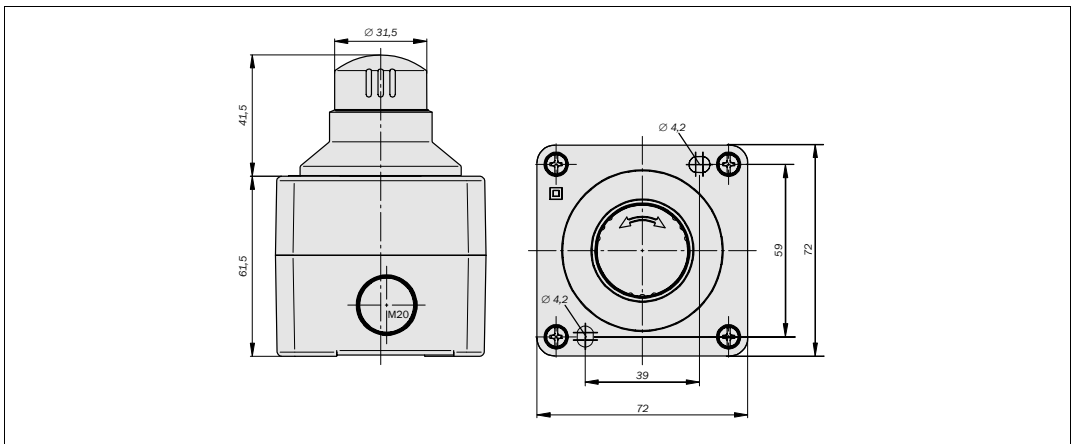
Croquis de dimensiones de la versión de montaje superficie (mm)
